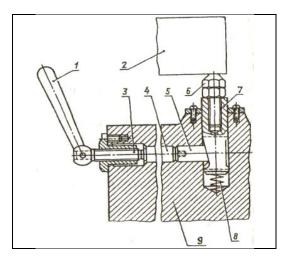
Индивидуальная стандартная самоустанавливающаяся опора
